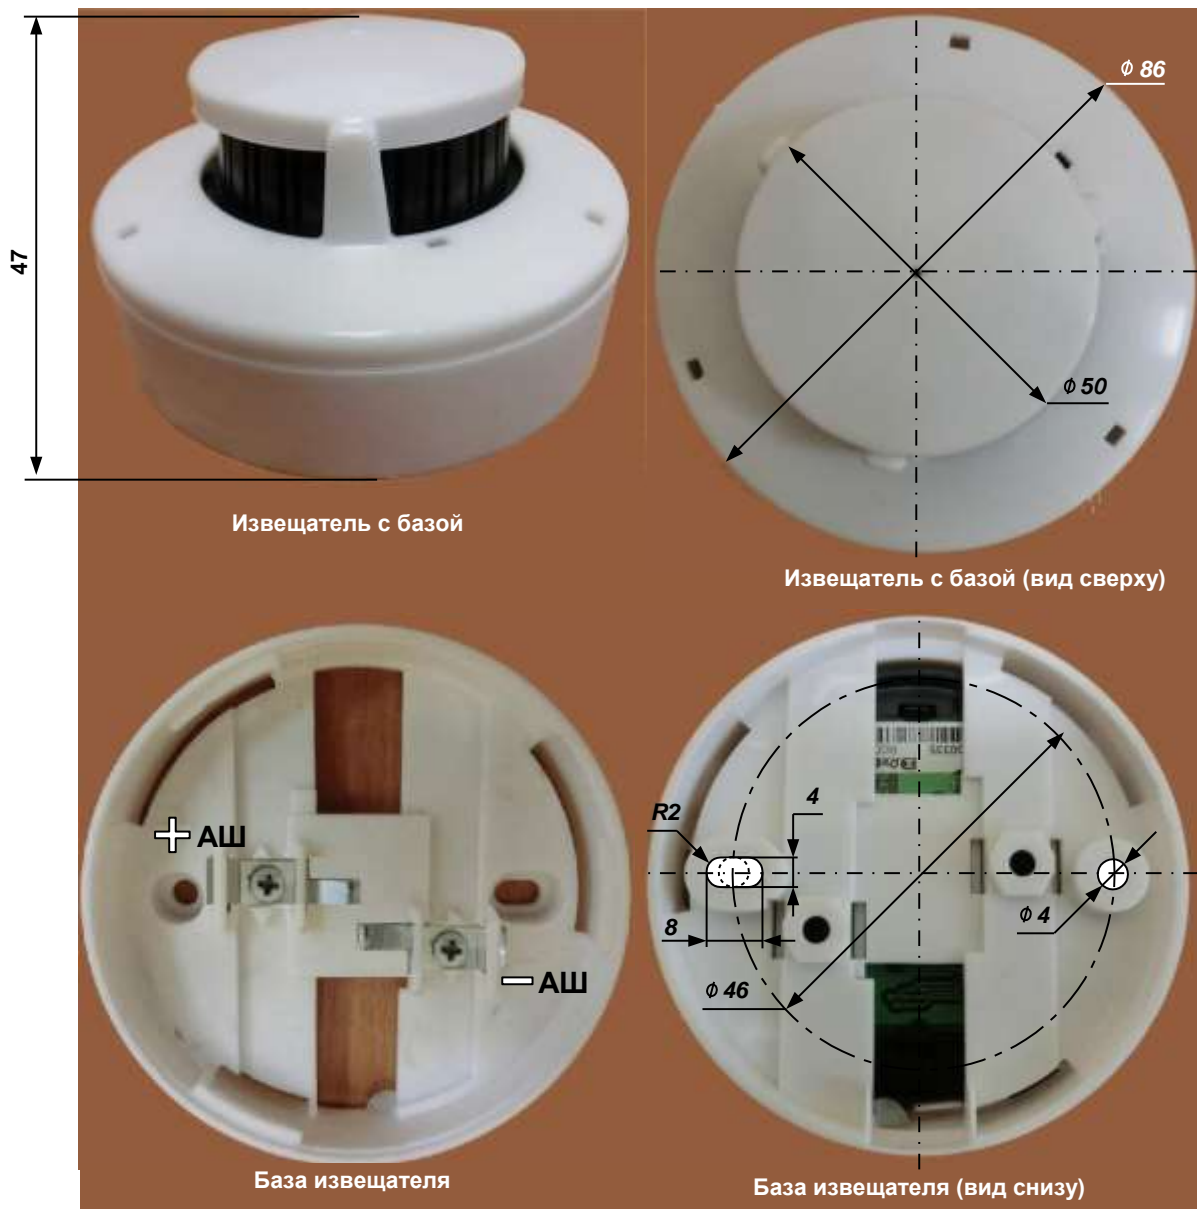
АЗДПИ. Извещатель с базой. Габаритные и присоединительные размеры.
